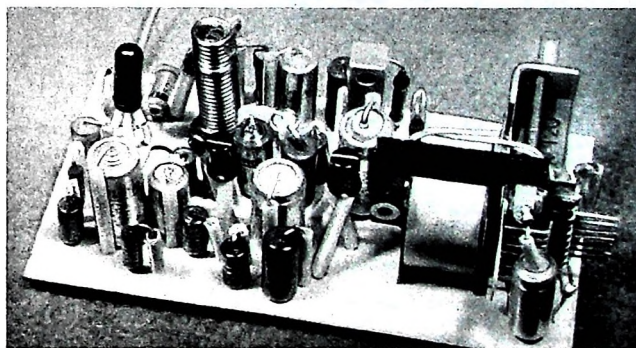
Ansicht des einbaufertigen Fernsteuerempfängers
